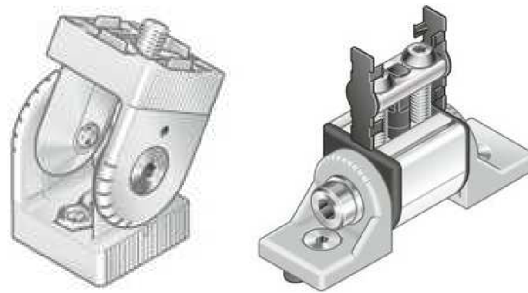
Úhelníky pro spojení profilů. [zdroj: Bosch Rexroth]
